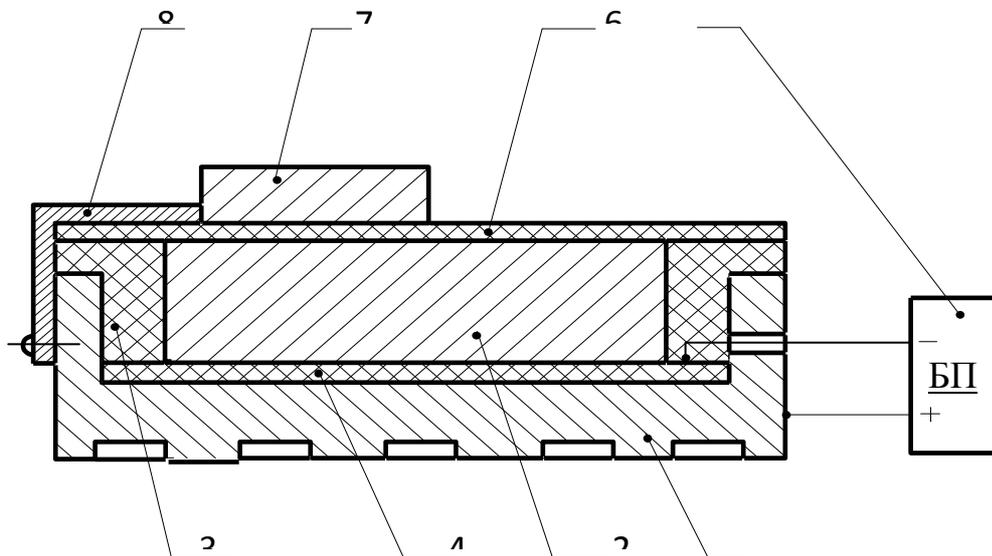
Схема электростатической плиты.: 1- корпус; 2 – полупроводящее тело; 3 – изолирующий контакт; 4 – фольгированный стеклотекстолит; 5 – блок питания; 6 – диэлектрическое покрытие; 7 – закрепляемая деталь; 8 – контактный угольник.
